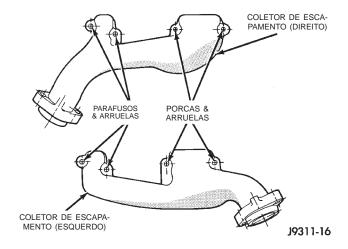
Instalação do Coletor de Escapamento — Motor 3.9L
